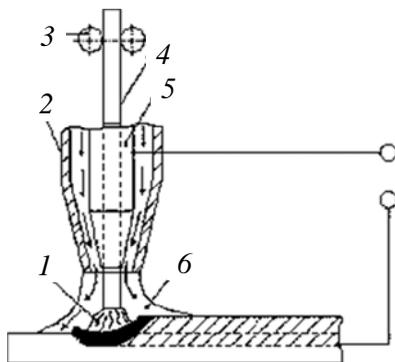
Схема электродуговой сварки (наплавки)
